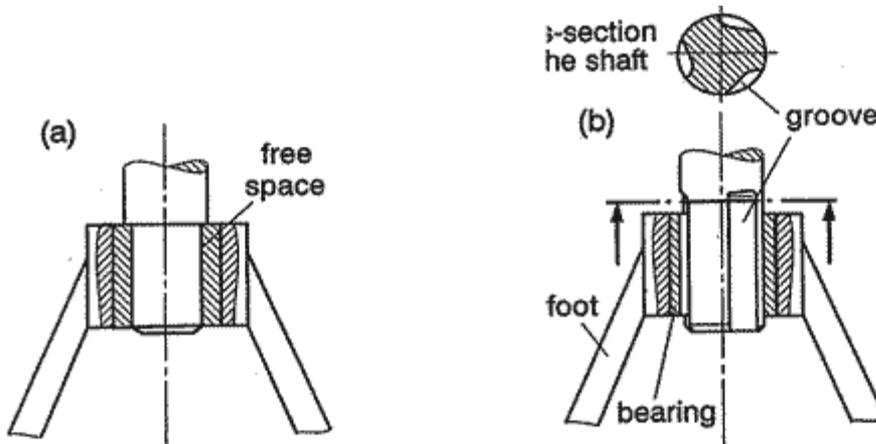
Проектирование опорных устройств. (a) опорное устройство с гладкой поверхностью или (b) опорное устройство с проточными канавками для очистки и стекания смазки.
